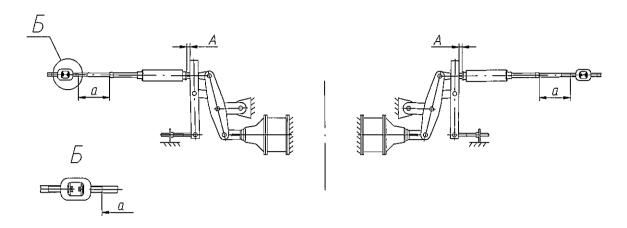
Схема установки на вагоне регулятора тормозной рычажной передачи с рычажным приводом
